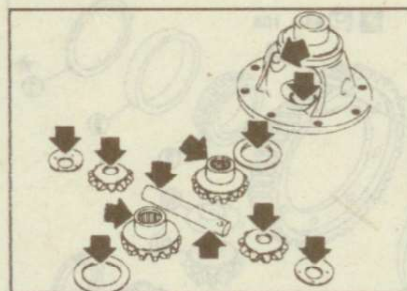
Проверка шестерен, шайб, оси и коробки дифференциала
